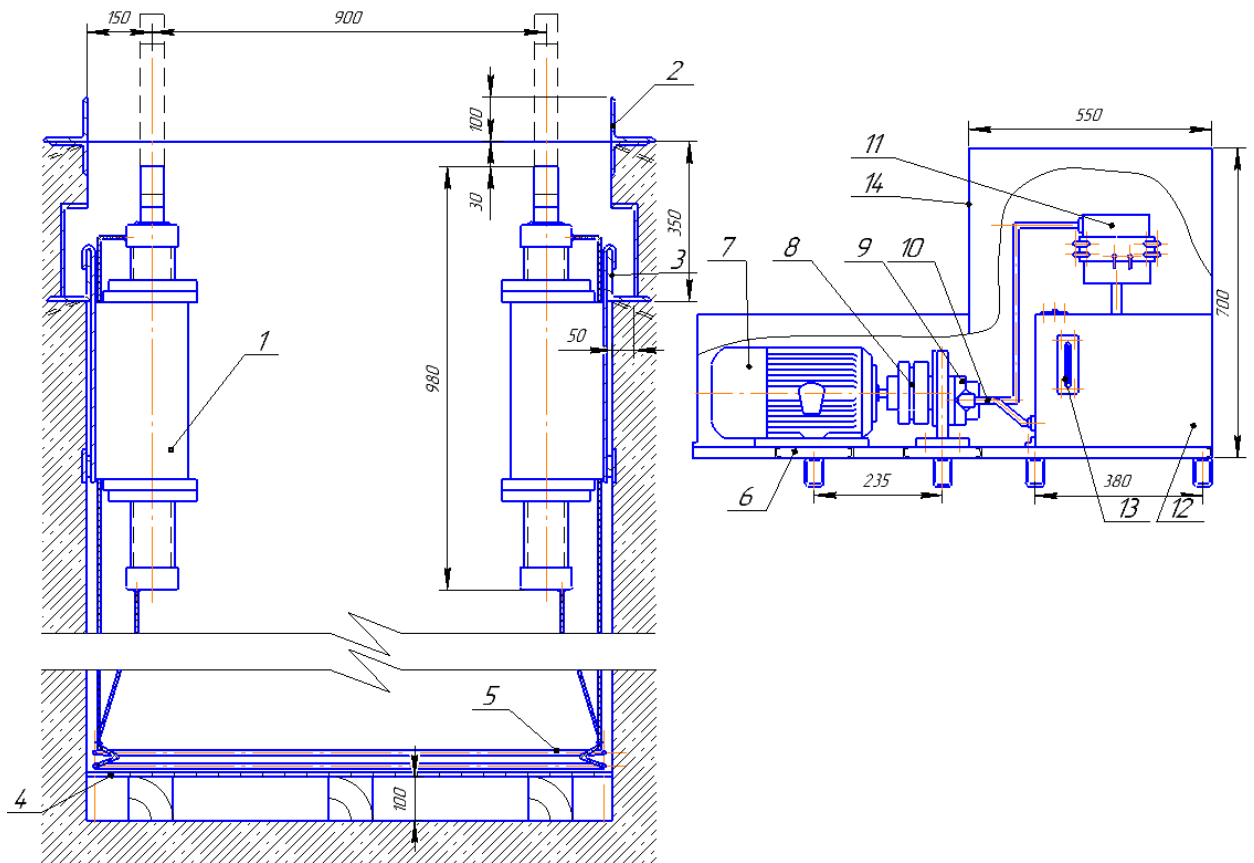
Загальний вид конструкції станда: 1 – Установа гідроциліндра; 2 – Обрамлення ями; 3 – Закладний елемент; 4 – Щит настила; 5 – Розводка гідросистеми; 6 – Рама; 7 – Електродвигун; 8 – Муфта; 9 – Насос шестеренчастий; 10 – Трубопроводи; 11 – Гідророзподільник; 14 – Бак масляний; 15 – Показник масла; 16 – Кожух
